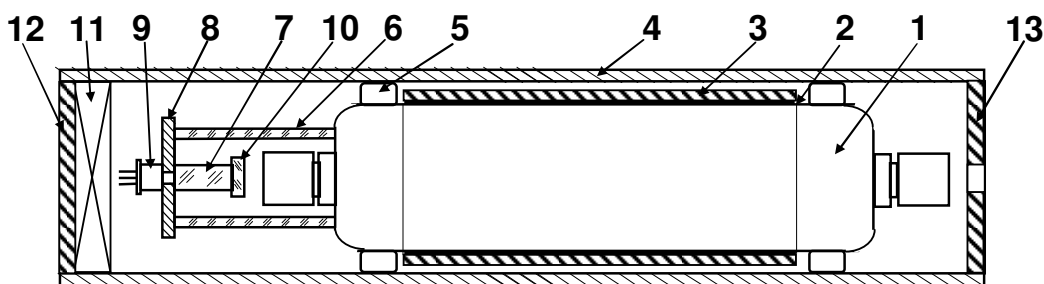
Конструкция излучателя лазера ЛГН-303.
